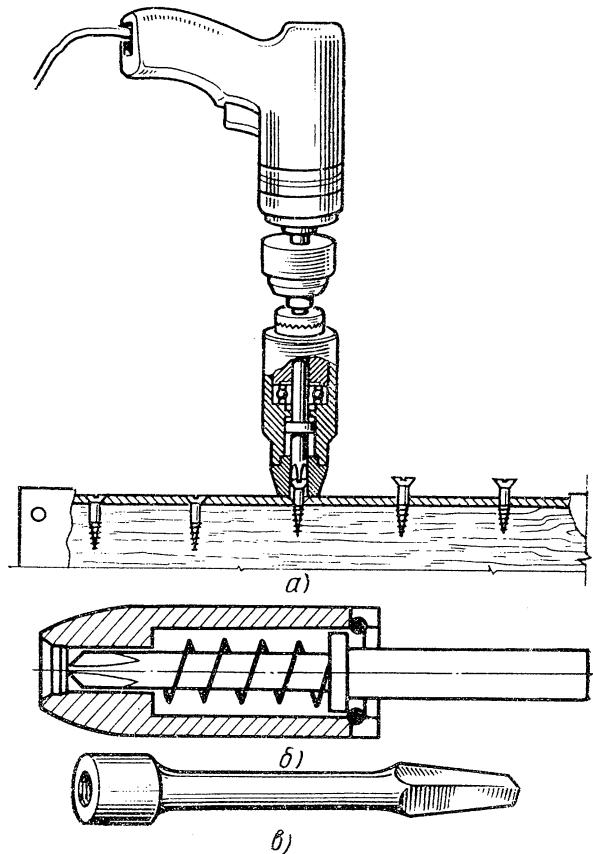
Завинчивание шурупов пневматическими сверлильными машинами (а); насадки для завинчивания шурупов (б) и шпилек (в)
